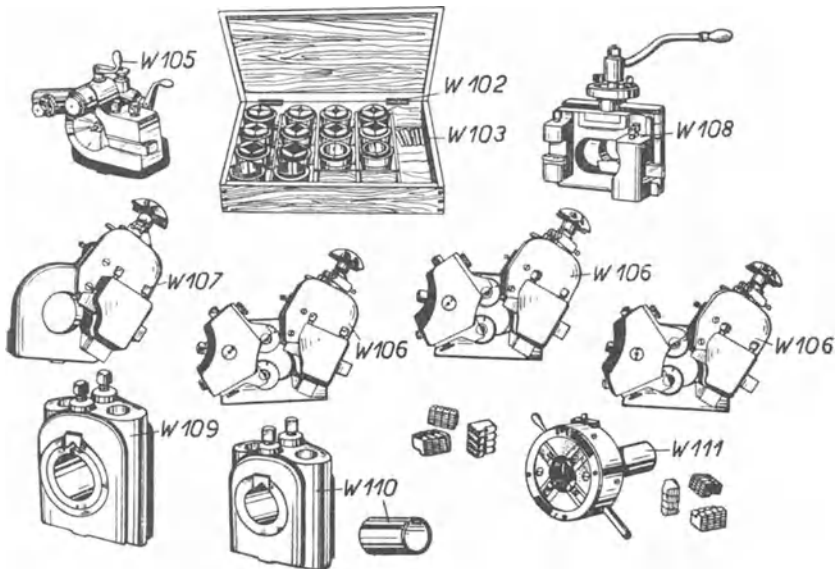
Stangenwerkzeuge für Tischrevolverbänke.
